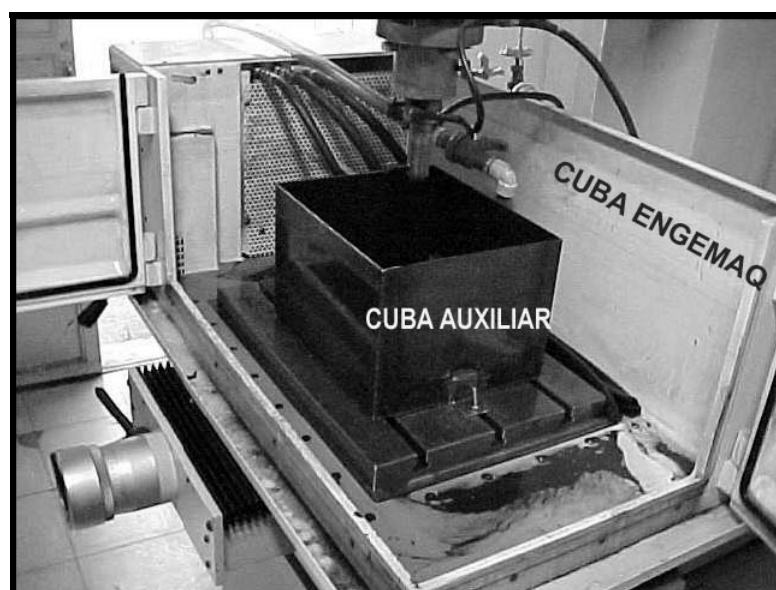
Máquina de usinagem por descargas elétricas (EDM) por penetração - Engemaq 440 NC.
